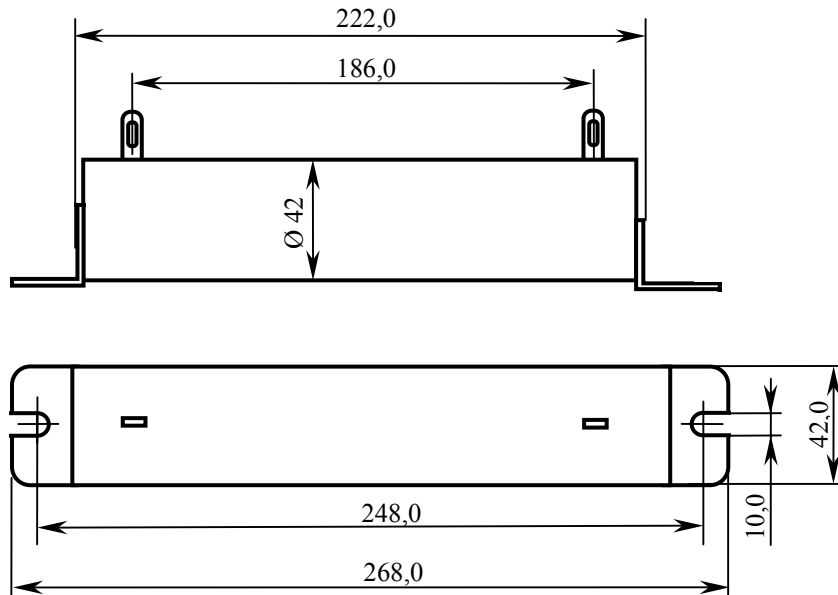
Габаритные и установочные размеры тормозного сопротивления RXHG 30RJ 200W
